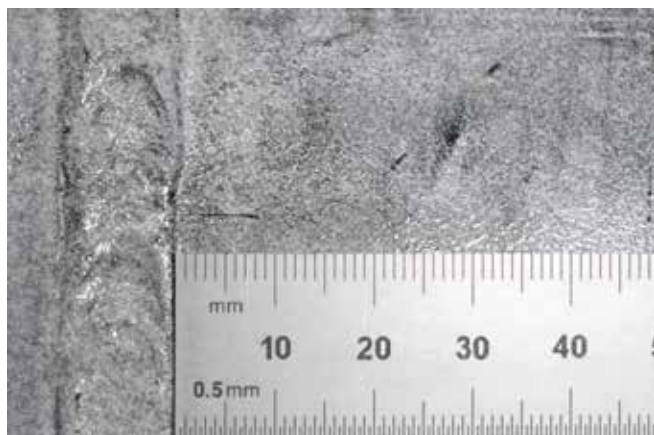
Fissure vue sur la surface intérieure de la conduite
